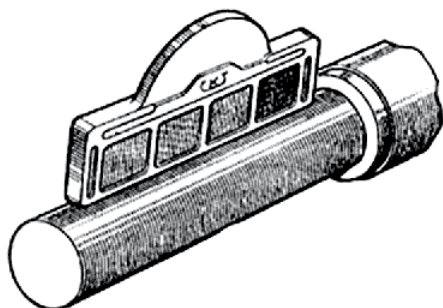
Образец шероховатости при визуальном контроле вала
